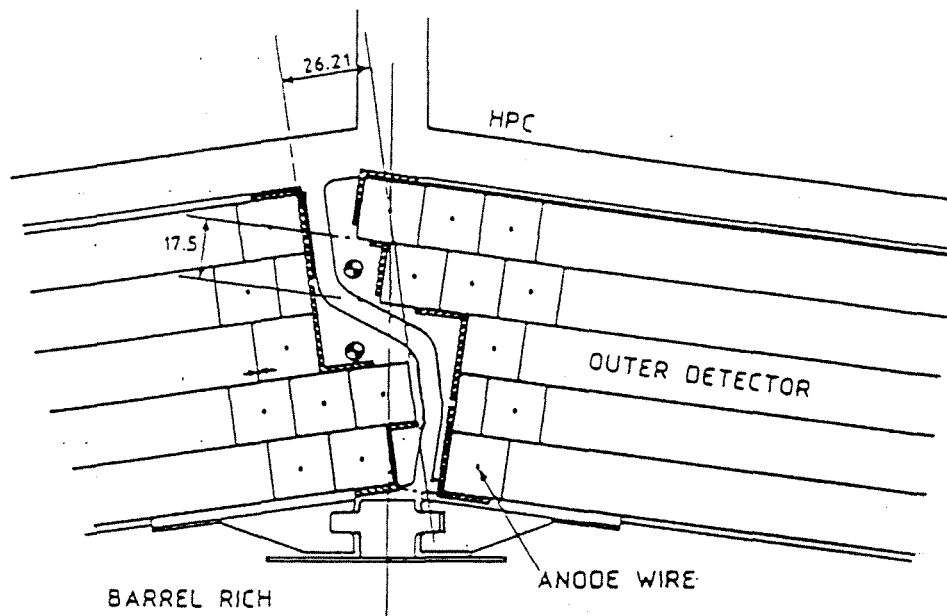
Detalle de la zona de solapamiento entre dos planchas del OD.
